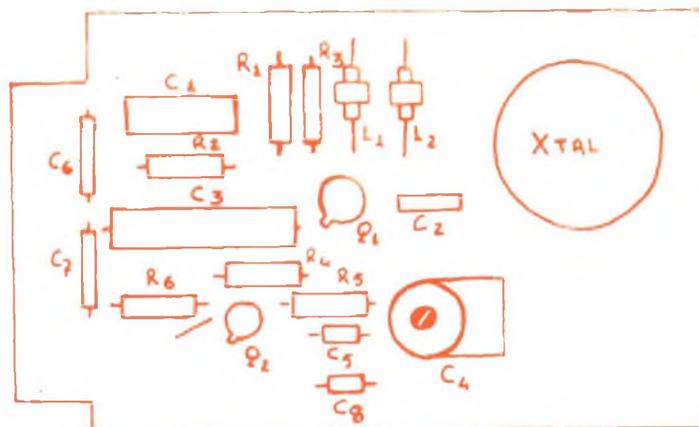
Circuito stampato visto dal lato sul quale si sistemano tutti i componenti.
